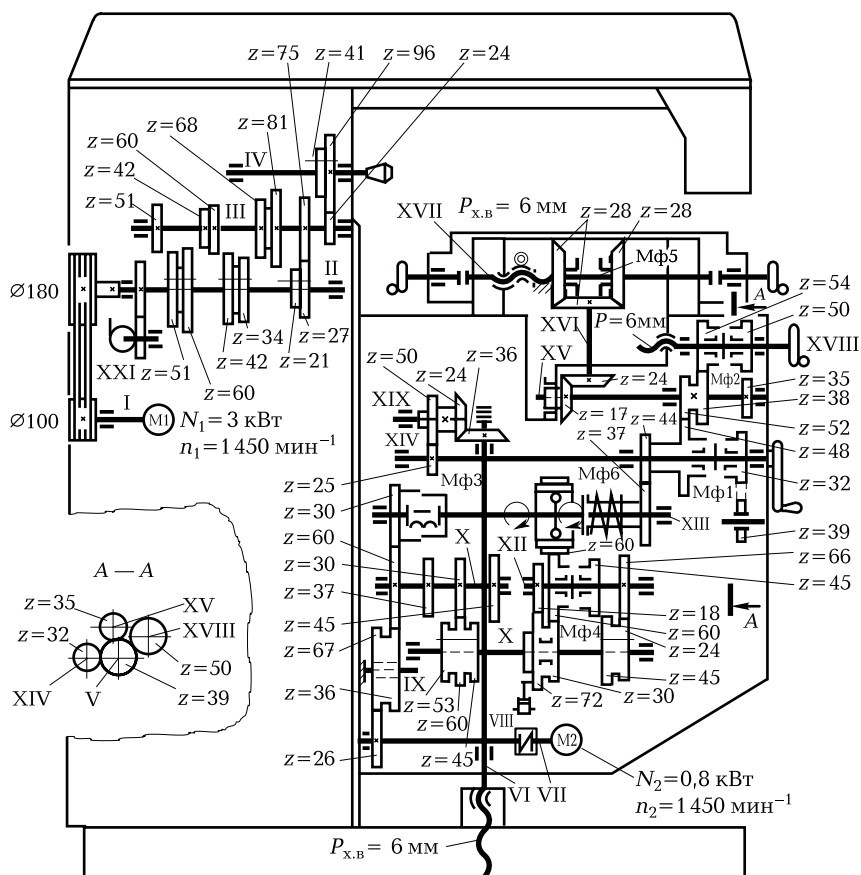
Кинематическая схема горизонтально-фрезерного консольного станка:
